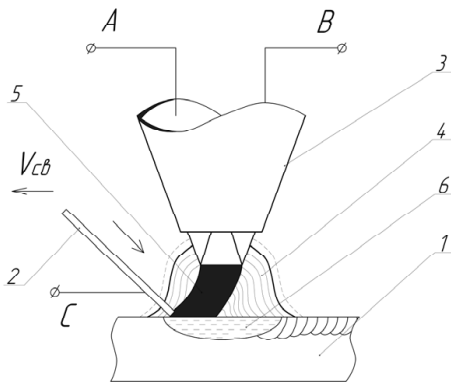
Схема сварки трехфазной дугой неплавящимся электродом: 1 – деталь; 2 – присадочная проволока; 3 – сварочная горелка; 4 – газокINETическая составляющая дуги; 5 – электродинамическая составляющая дуги; 6 – сварочная ванна
